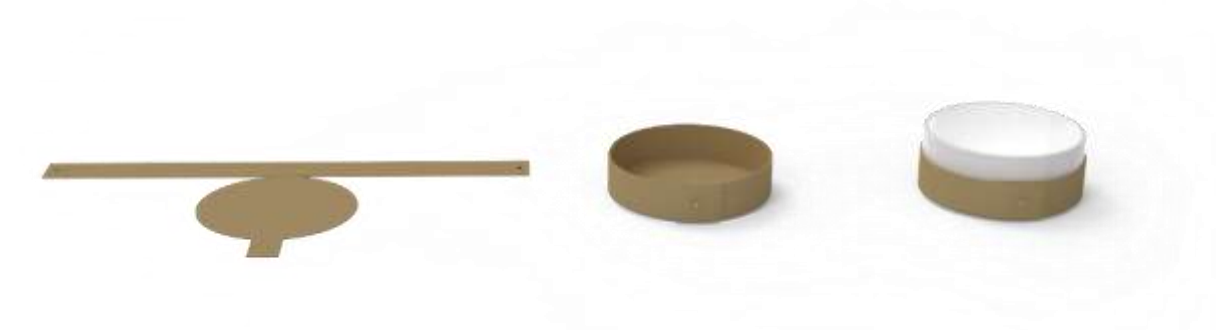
Porta ciotole "Icché c'è c'è", modalità di assemblaggio delle componenti.
